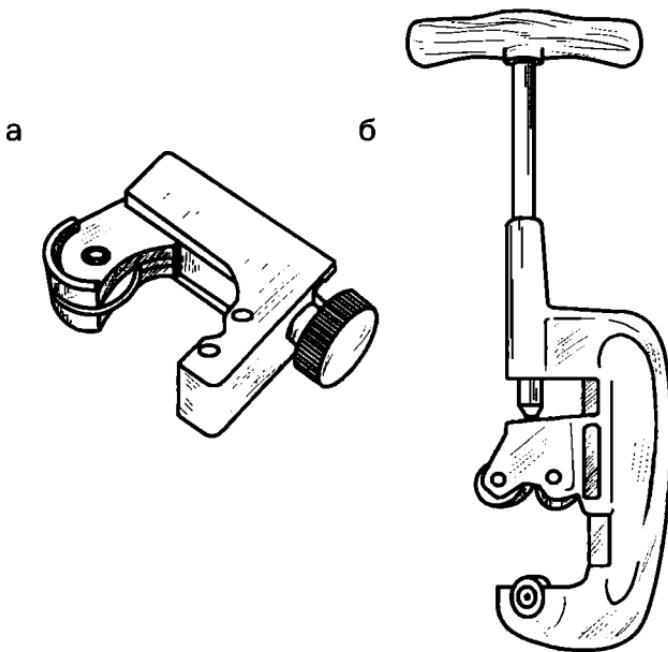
Труборезы: а — для медных труб; б — для стальных труб
